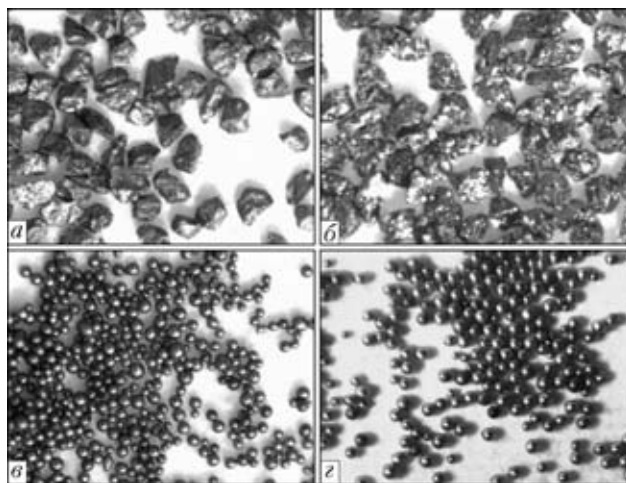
Внешний вид частиц карбида вольфрама ( $\times 80$ ), полученных по различным технологиям: а — дробленый; б — макрокристаллический; в, г — соответственно сферический и распыленный
